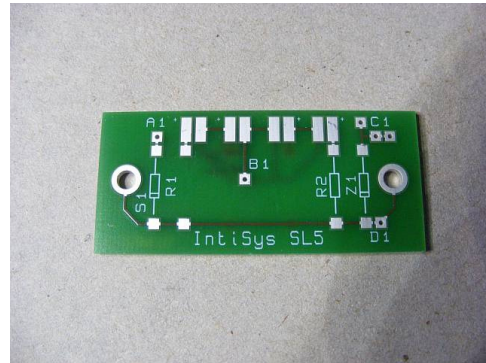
Epoxy-Platine zum Auflöten der Bauteile
